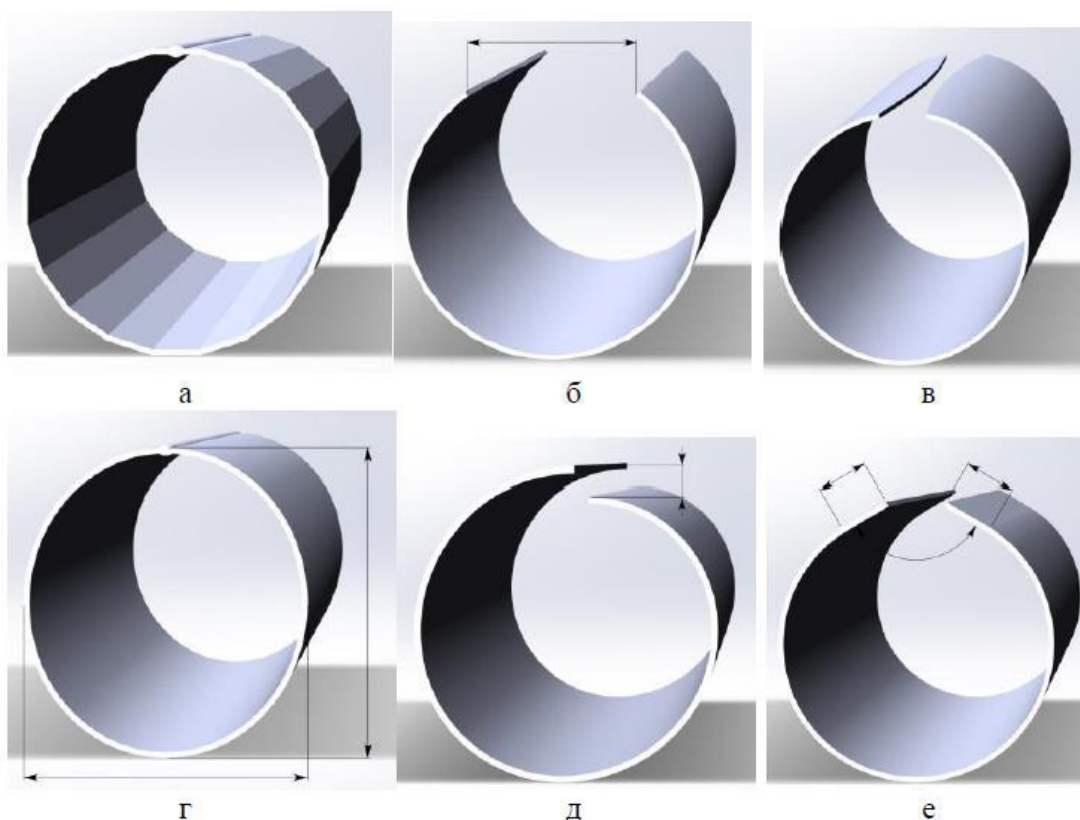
Типовые дефекты труб, трубной заготовки после формовки:
